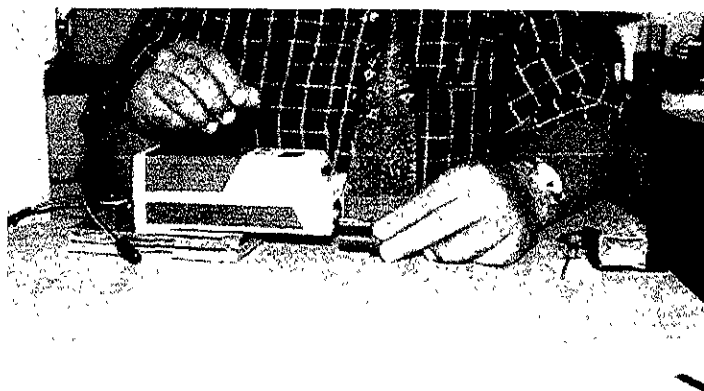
Medición de Rugosidad (Rugosímetro de la Universidad Panamericana).
